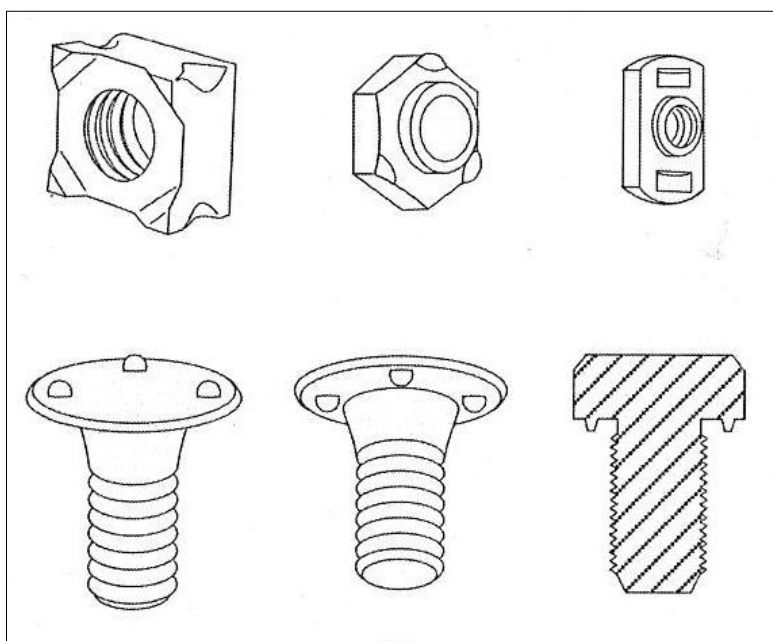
Diferentes tipos de tuercas y tornillos aptos para soldadura por proyección.
